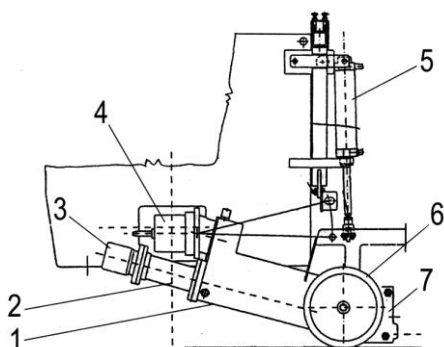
Конструктивная схема экструдера для маркировки пластиками:
